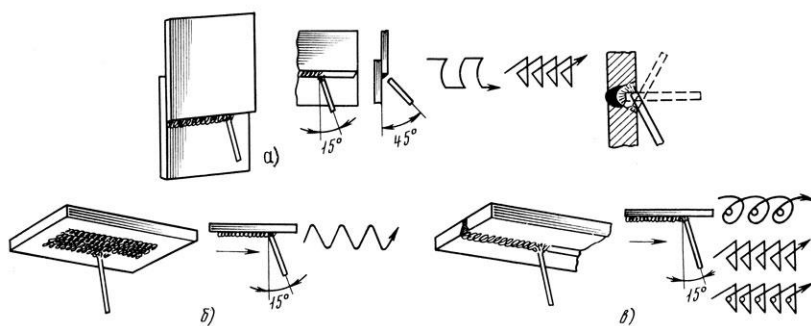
Положение и движения электрода при сварке в горизонтальном и потолочном положениях: а - горизонтальный угловой шов, б - наплавка в потолочном положении, в - потолочный стыковой шов
